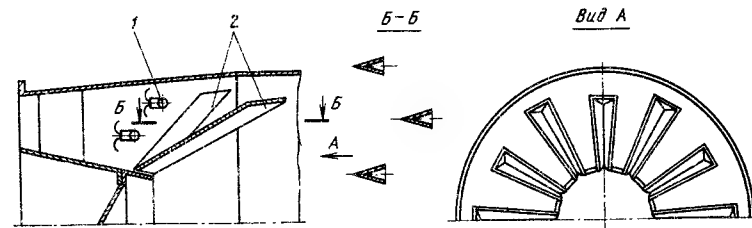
Схема фронтального устройства с радиальными стабилизаторами пламени: 1 — топливные коллекторы с форсунками; 2 — радиальные стабилизаторы пламени
